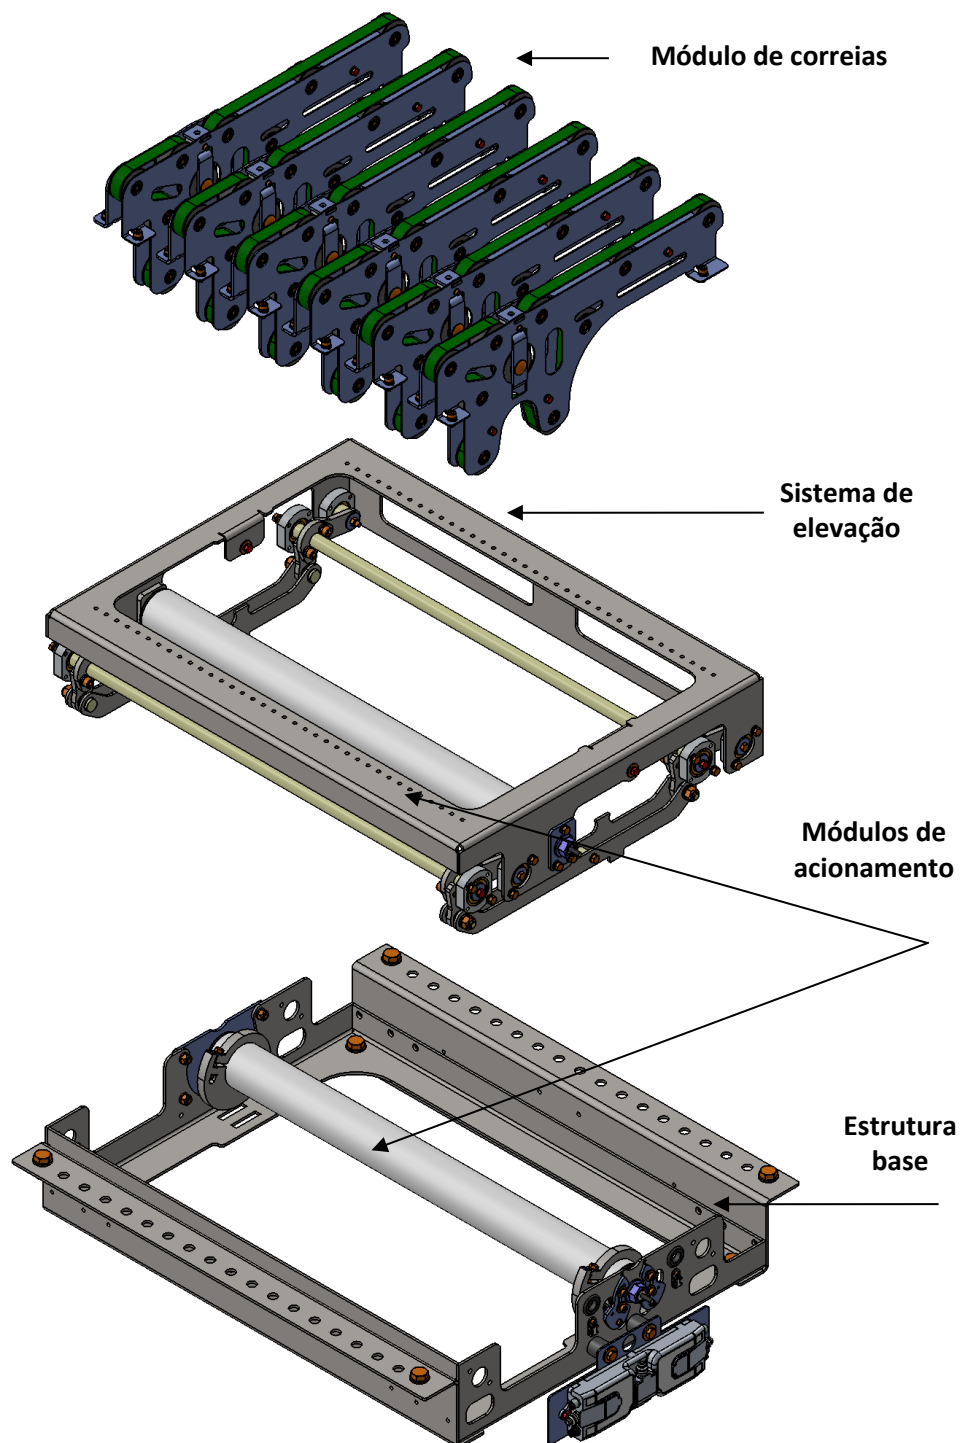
Vista explodida dos conjuntos constituintes do equipamento final
